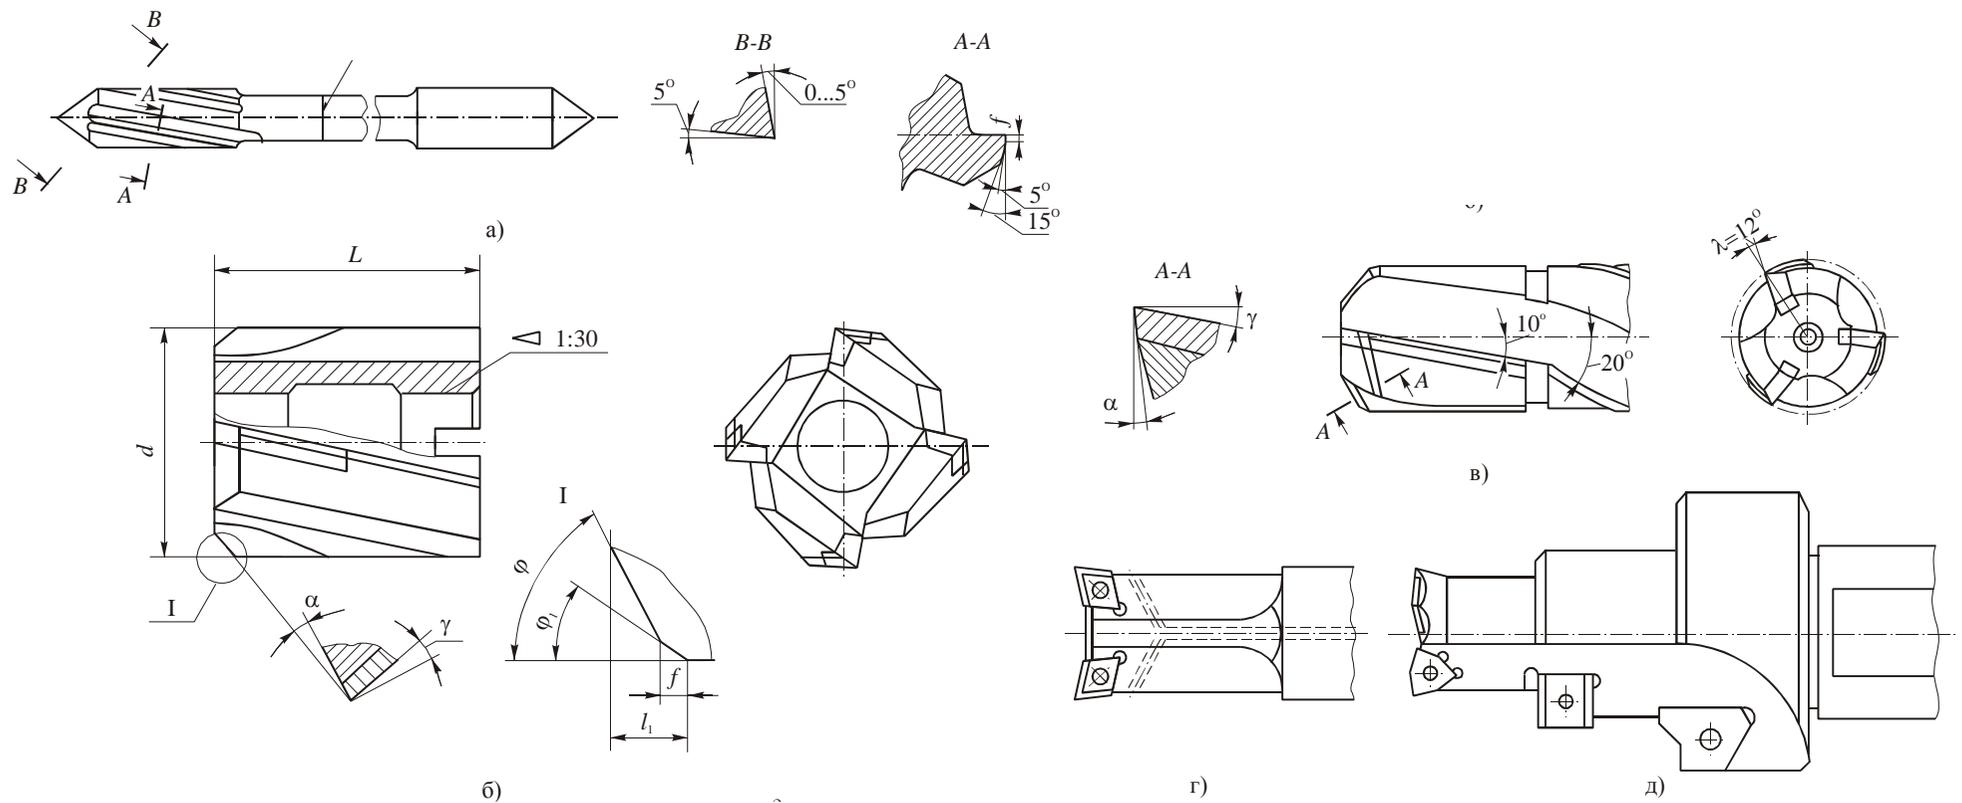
Твердосплавные зенкеры: *a* – цельный; *б* – насадной, с напайными твердосплавными пластинами; *в* – хвостовой, с напайными твердосплавными пластинами; *г* – с механическим креплением твердосплавных пластин и внутренним охлаждением; *д* – комбинированный зенкер-сверло
